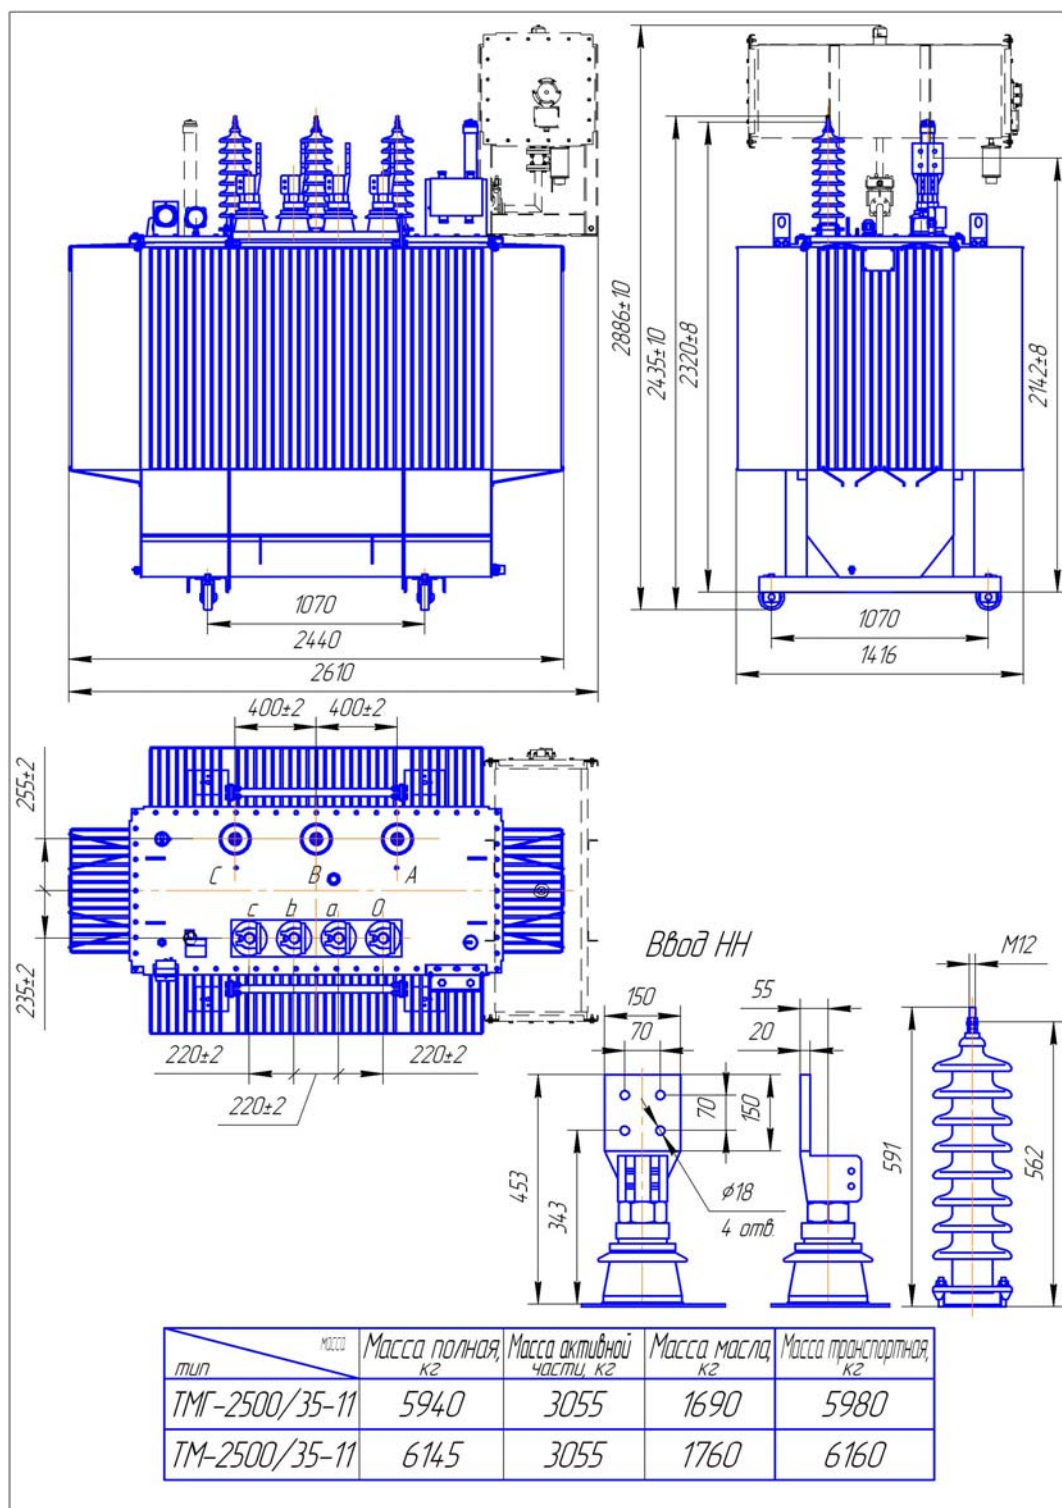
Габаритные, установочные и присоединительные размеры трансформатора ТМ(Г) - 2500/35-11
